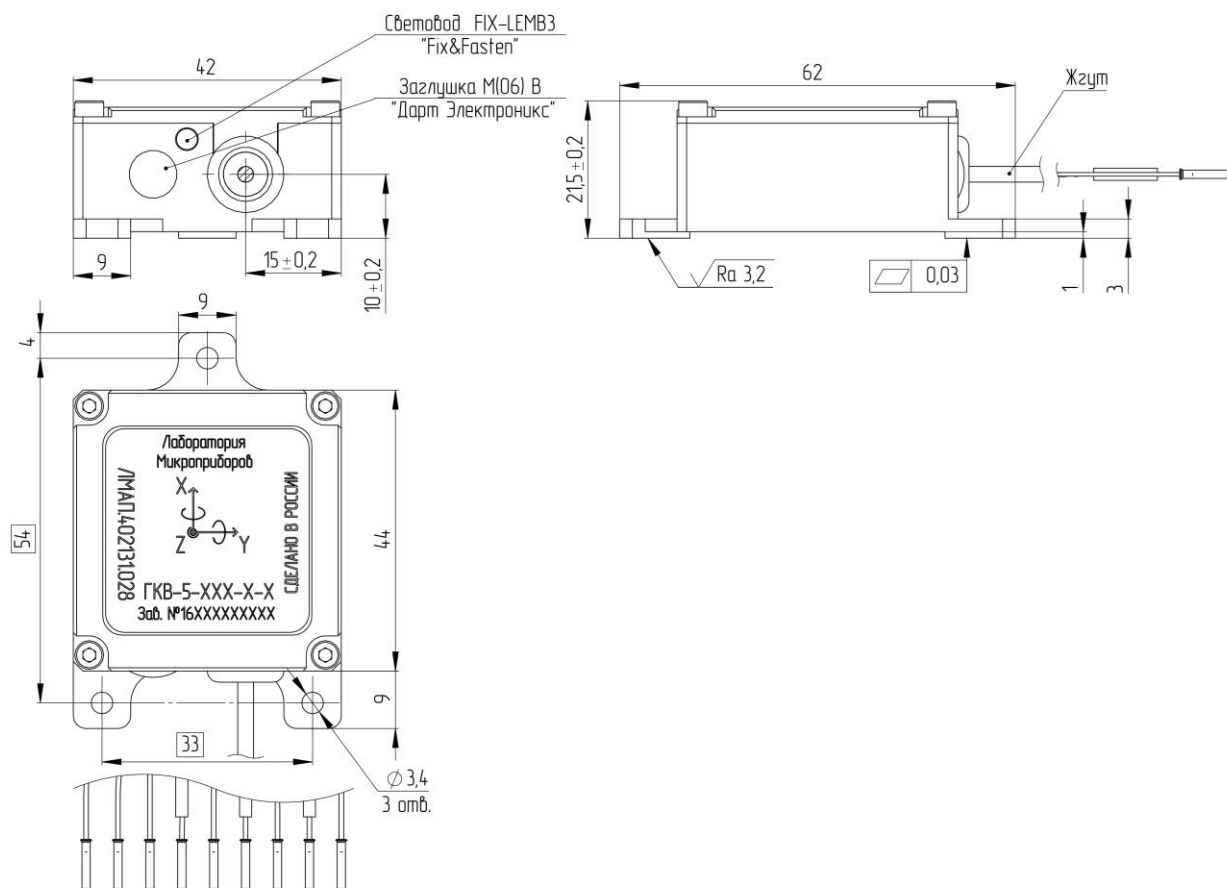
Габаритный чертеж ГКВ-5 ЛМАП.402131.028-02
